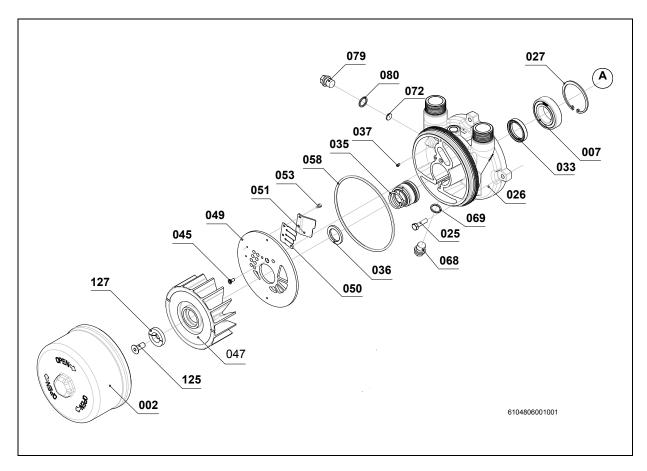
Disegno esploso: componente pompa per vuoto / compressore
